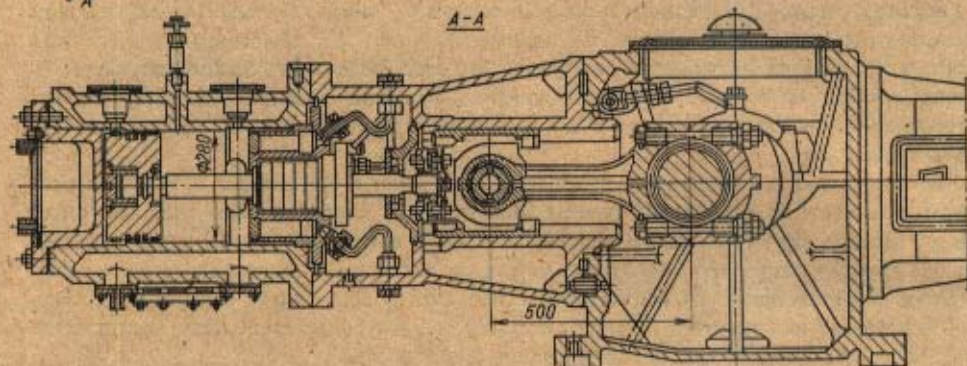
Поршневой оппозитный аммиачный одноступенчатый компрессор
